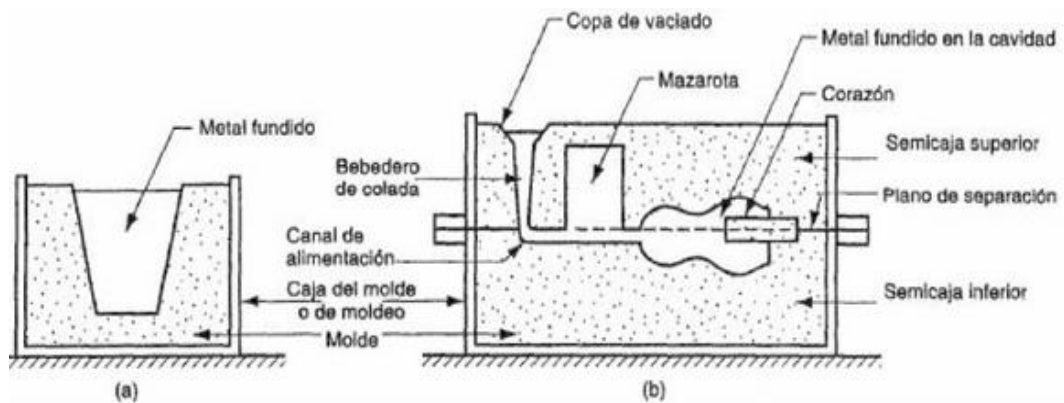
Proceso de fundición con molde abierto y molde cerrado 1
